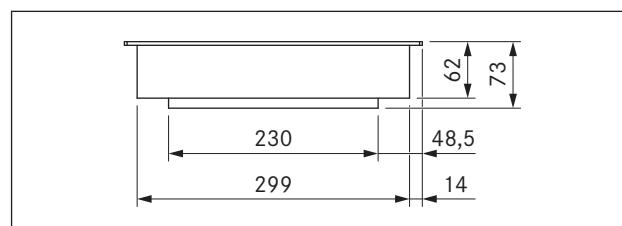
Dimensões do aparelho CKT, vista frontal
